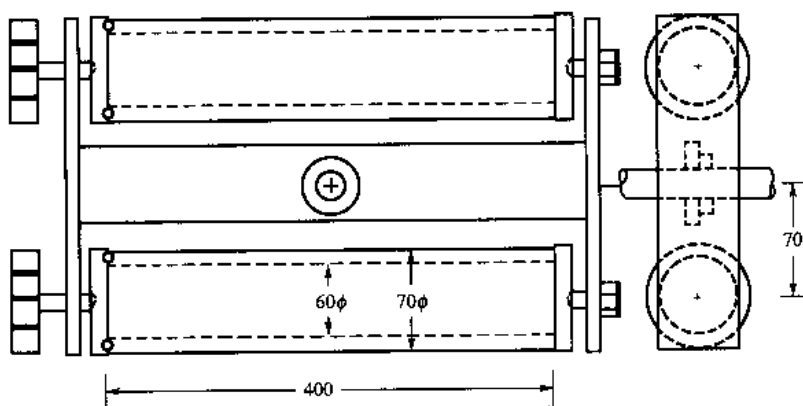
磨耗管样式(尺寸单位:mm)
